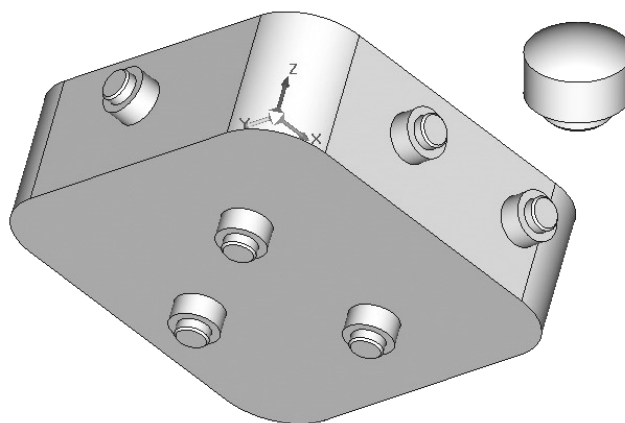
Базирование заготовки на шесть стандартных опор
